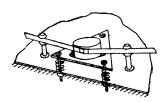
Способ механического крепления головки на подвижной регулировочной платформе.
